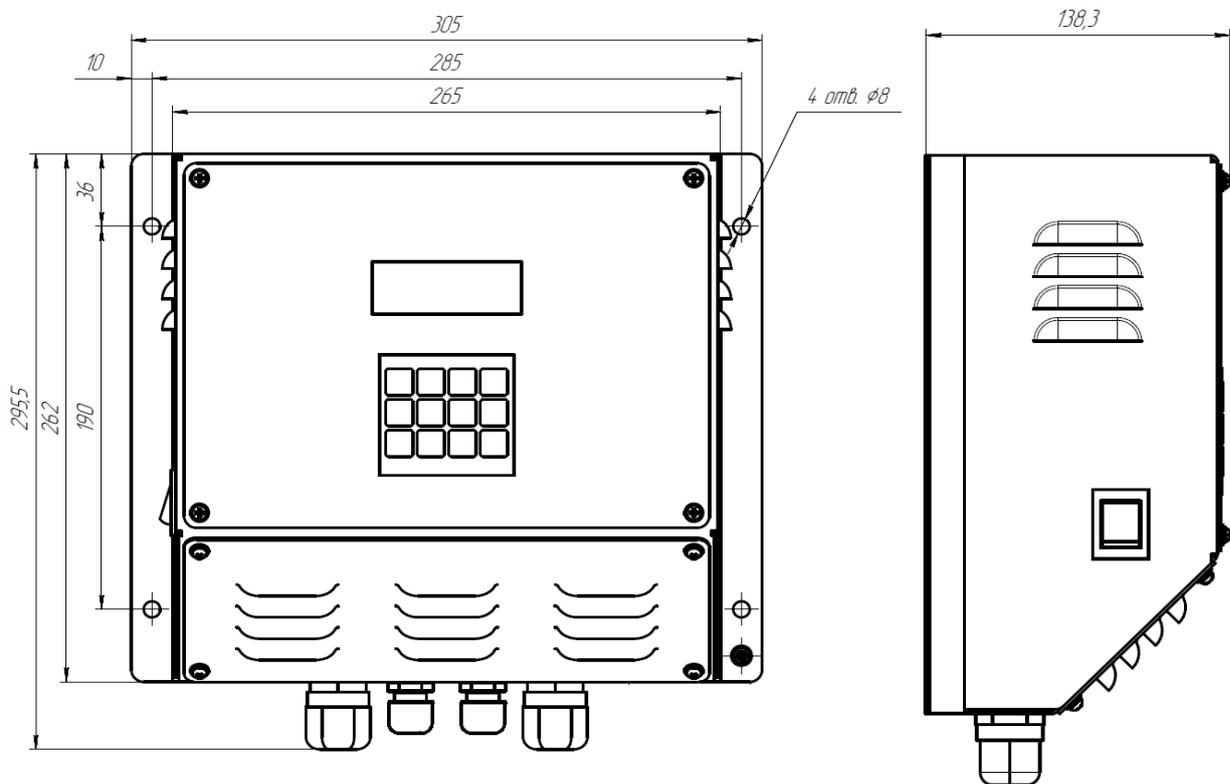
Общий вид и габаритные размеры изделия
